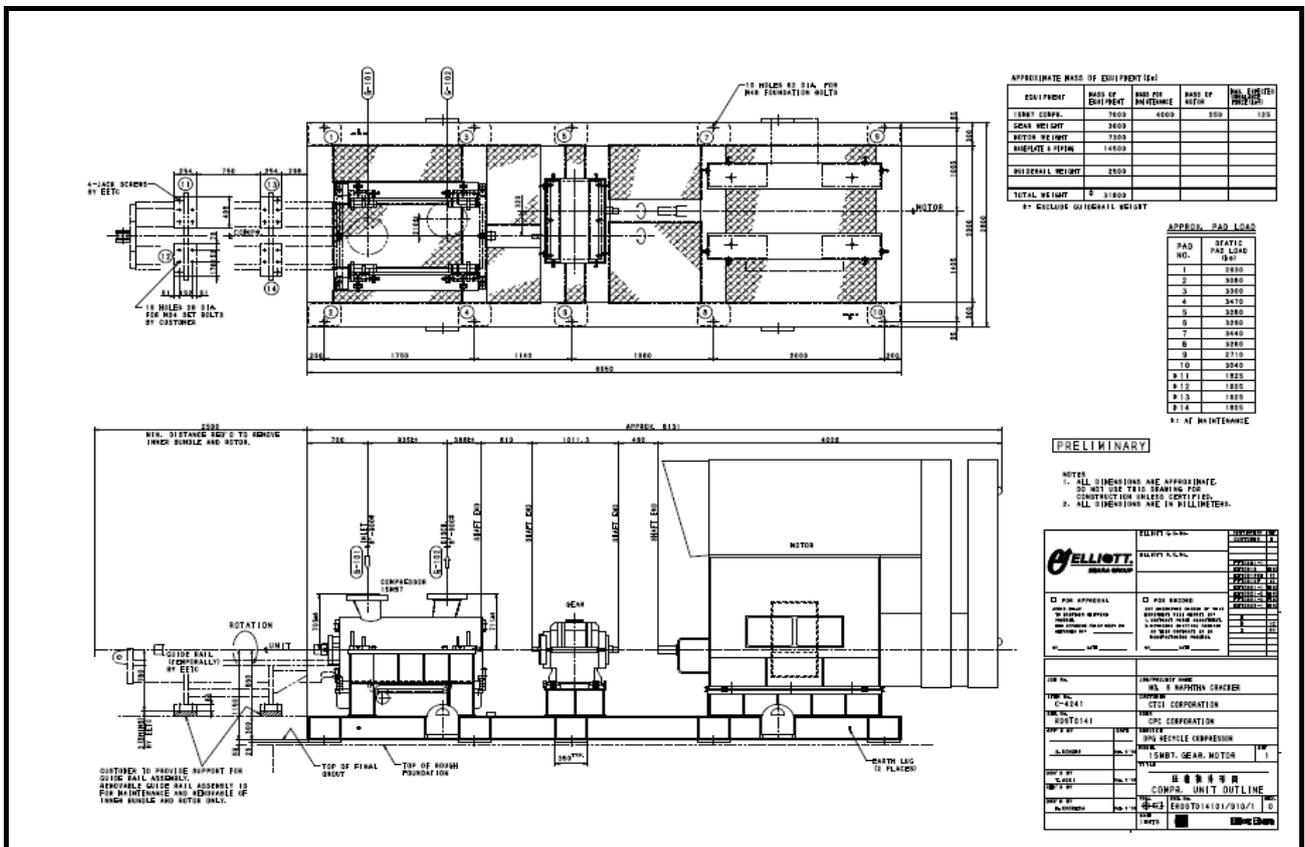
Turbo-Compressor Train—Outline Drawing
